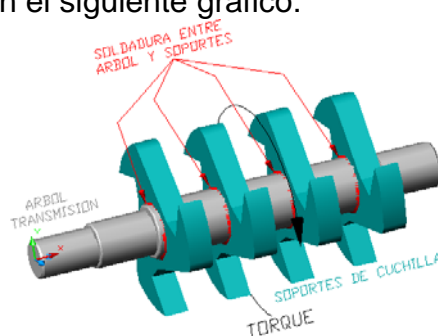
Soldadura entre soportes y árbol de transmisión
